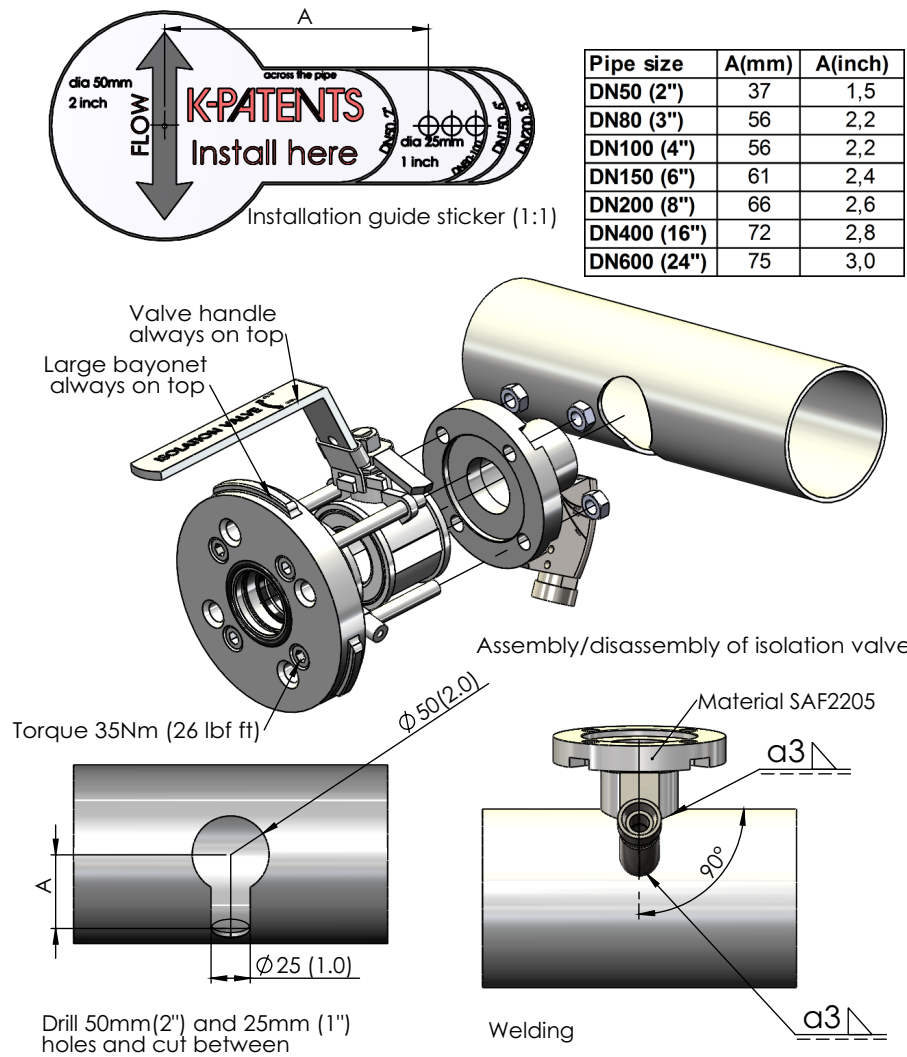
Soldadura de la válvula de aislamiento Safe-Drive™ a un tubo horizontal
